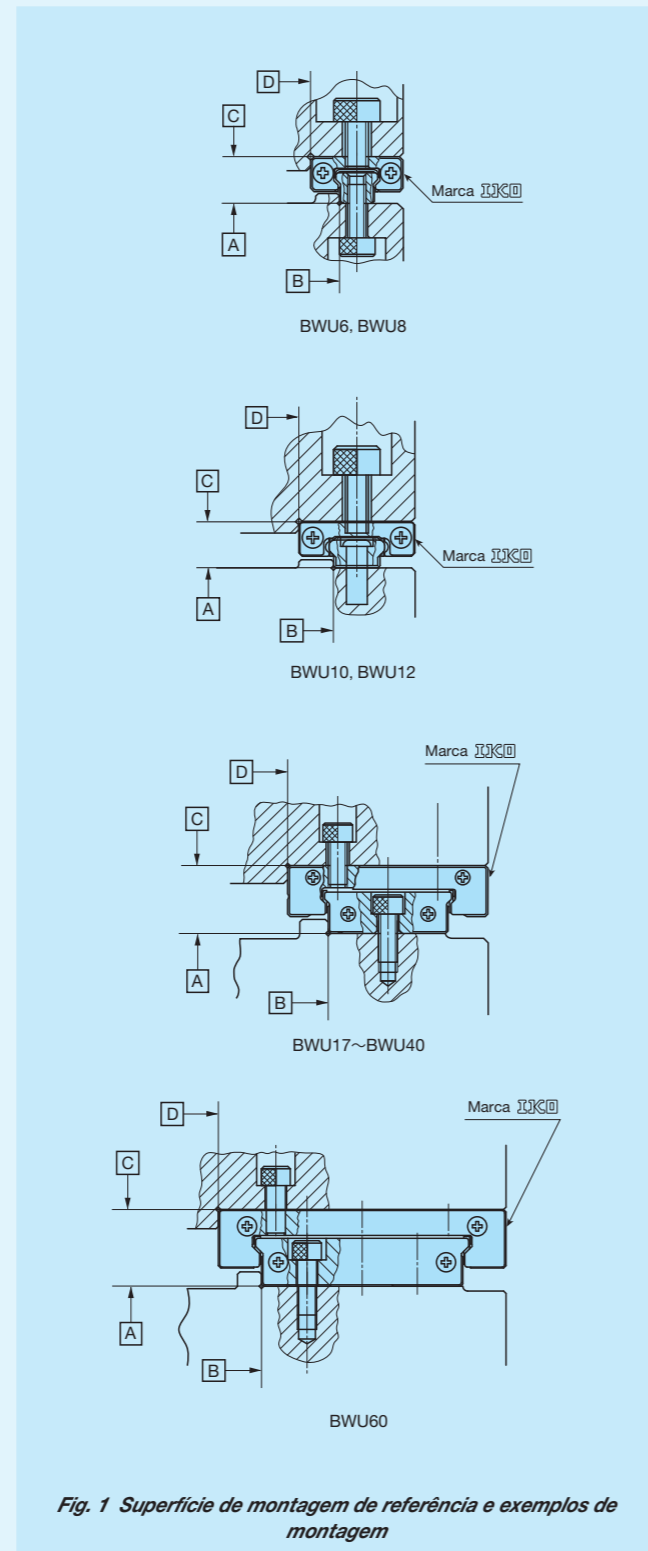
Superfície de montagem de referência e exemplos de montagem
